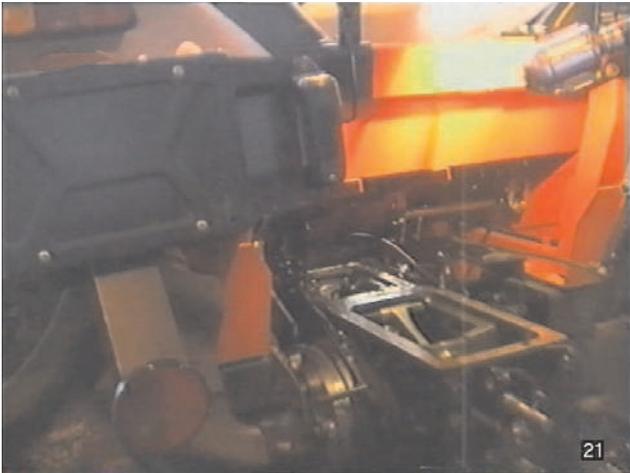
L'accès au démontage de l'embrayage de la P.d.F. arrière est possible sans le dépose de la cabine du tracteur. Désaccoupler les commandes des distributeurs hydrauliques auxiliaires.
